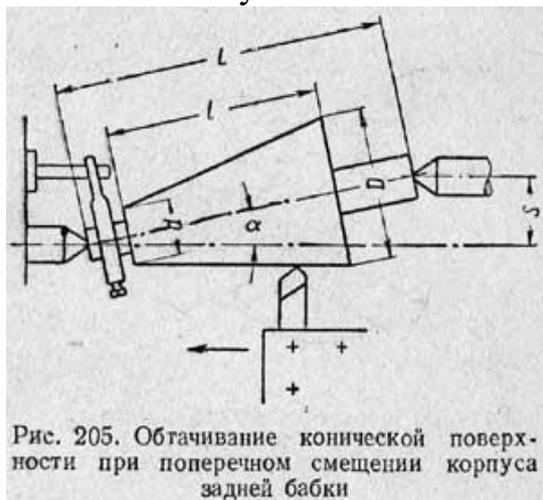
Обтачивание конической поверхности при поперечном смещении корпуса задней бабки
